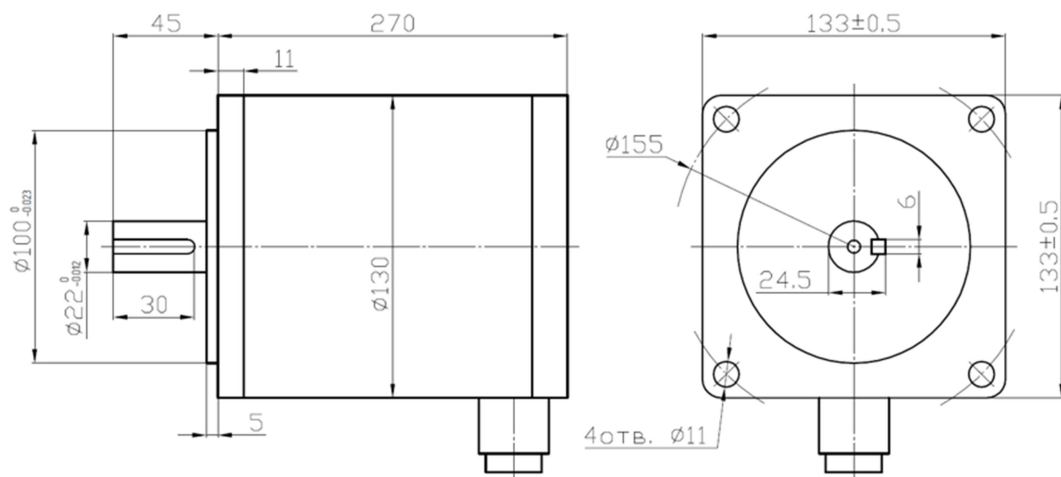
Габаритні розміри двигуна FL42STH33-0316A
